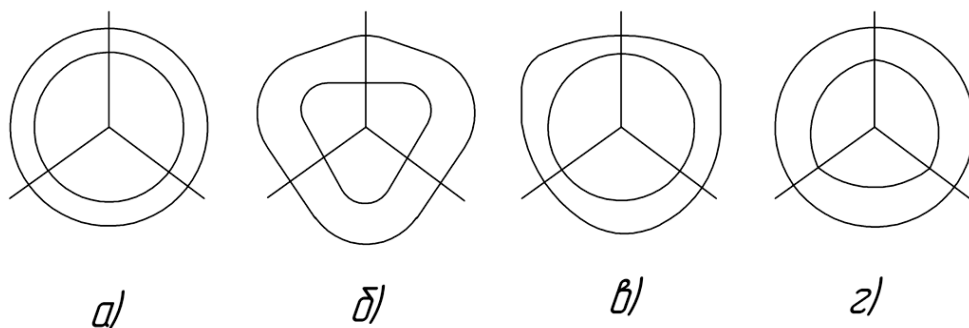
Схема образования погрешностей заготовки при обработке отверстия в патроне. Форма заготовки:
